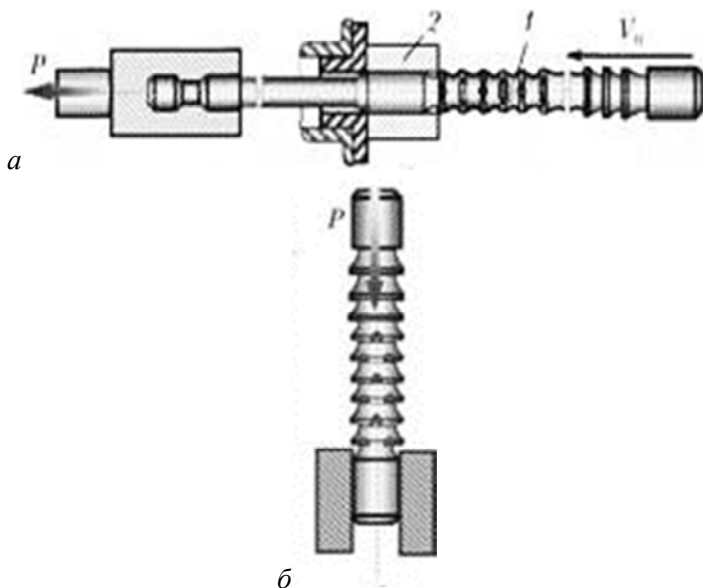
Схемы обработки протяжкой (*а*) и внутренней прошивкой (*б*)
